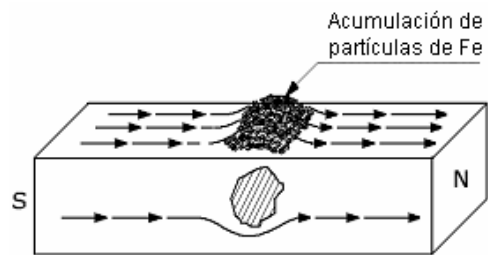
Aplicación de limaduras de hierro sobre componente de prueba
